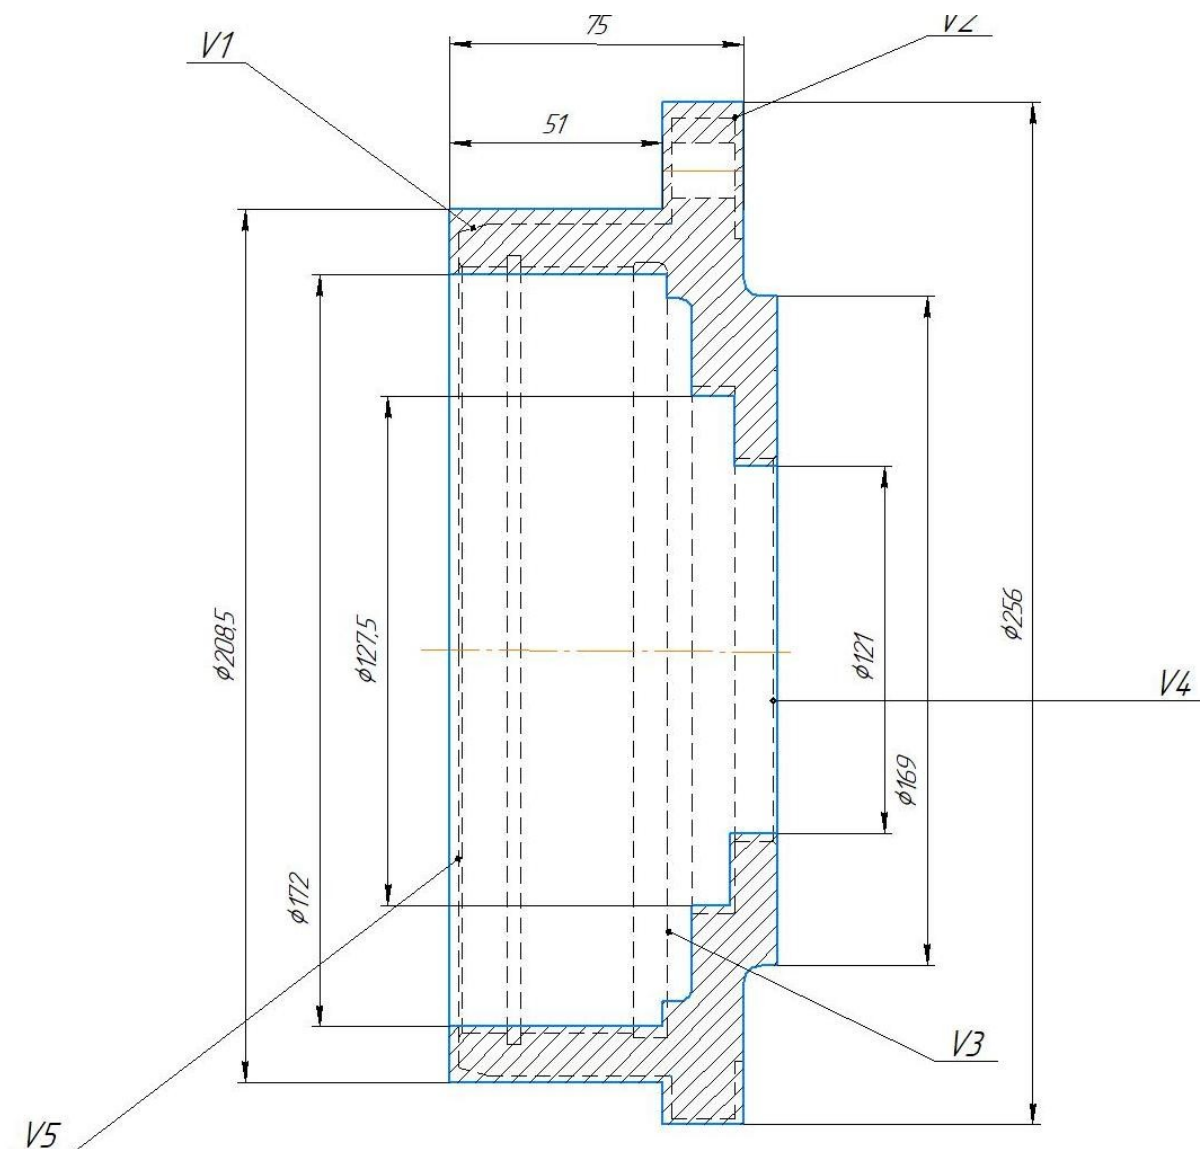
Эскиз заготовки детали Крышка ДЗ-98.1006.086
